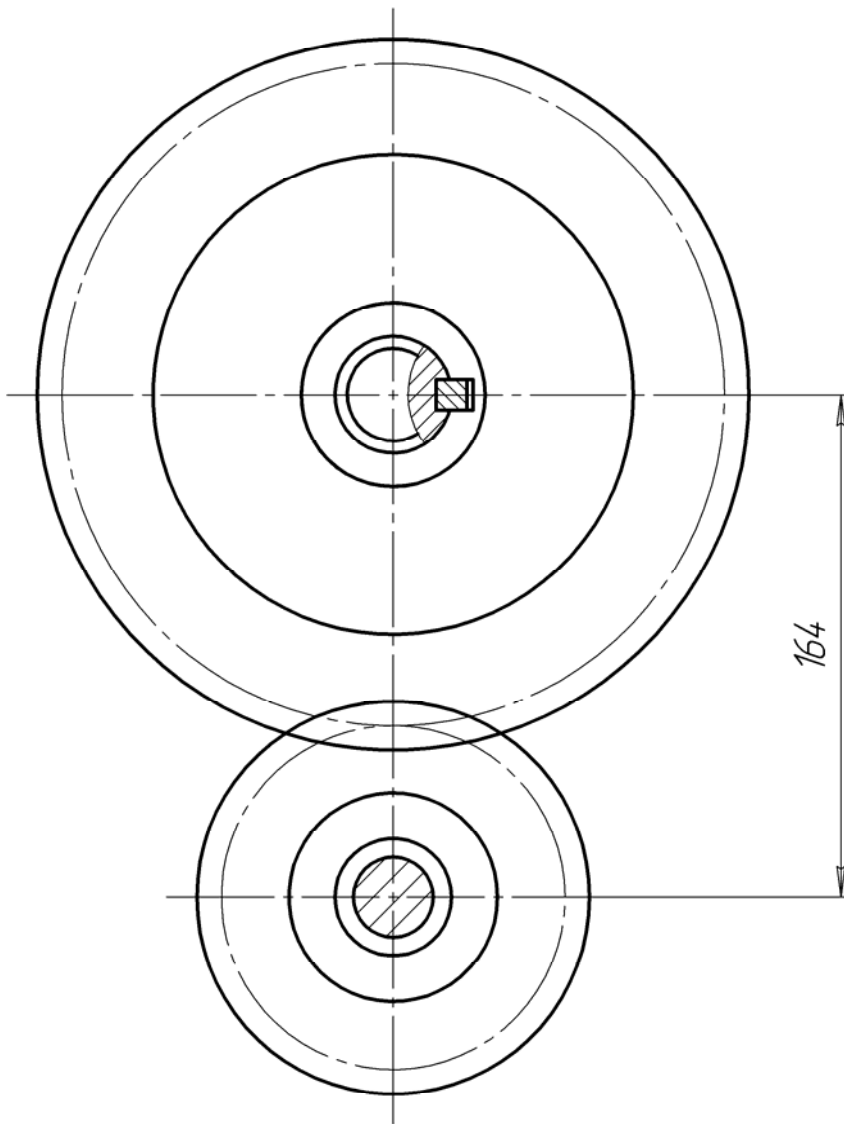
Сборочный чертеж зубчатой передачи с валом – шестерней
